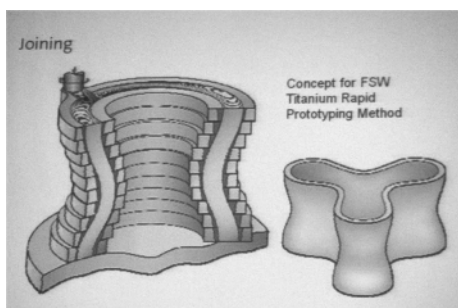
采用线摩擦焊接的 FSW 发动机构件
